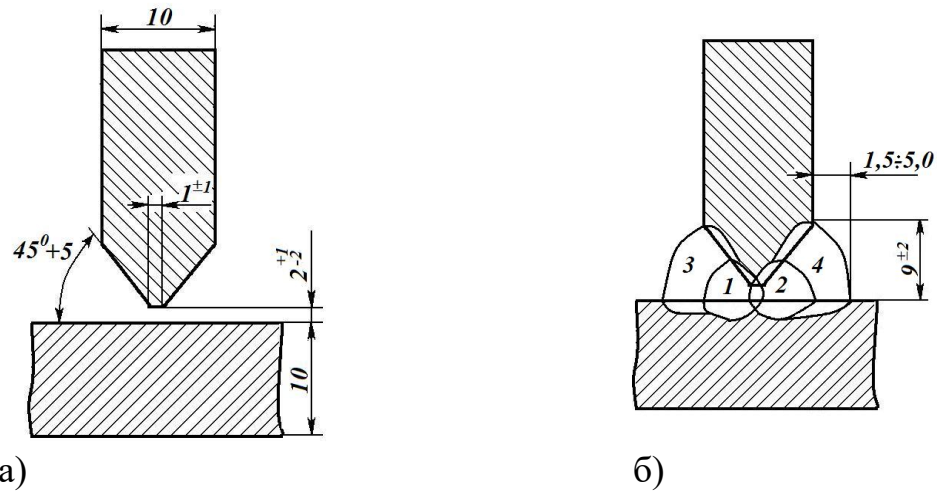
Конструктивные размеры и порядок заполнения разработки таврового соединения.
